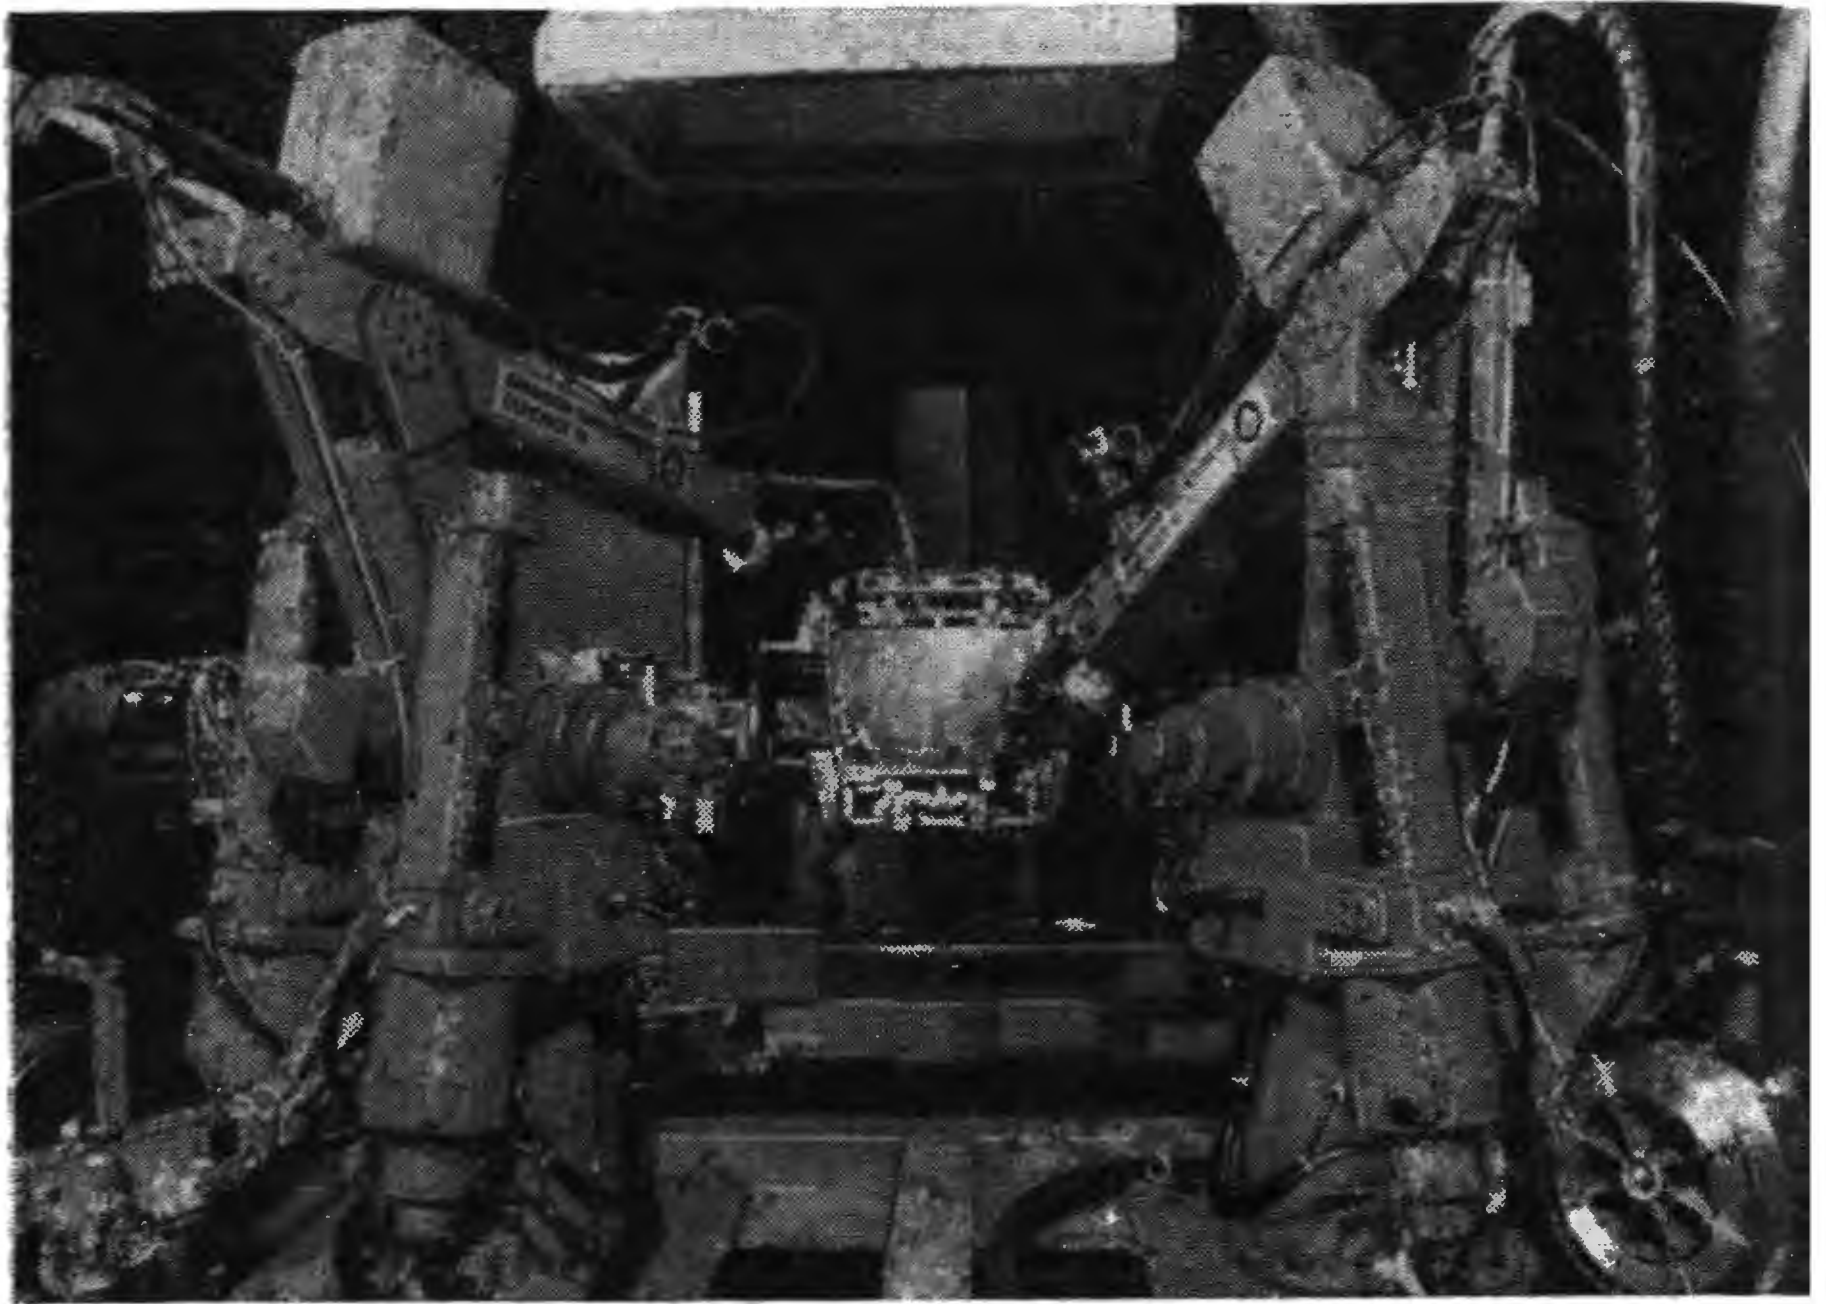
Дуговая сварка изделия одновременно двумя роботами
